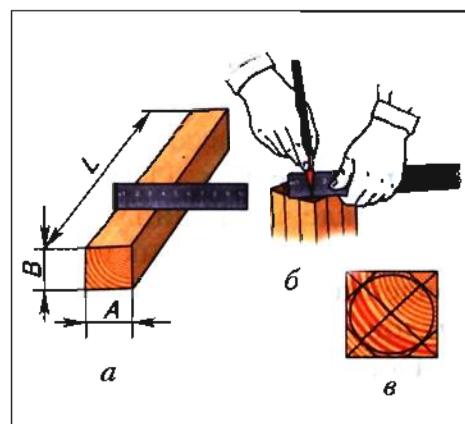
Подготовка заготовки для точения: а — измерение; б — разметка окружности, касательных и рёбер восьмикгранника; в — размеченный торец
